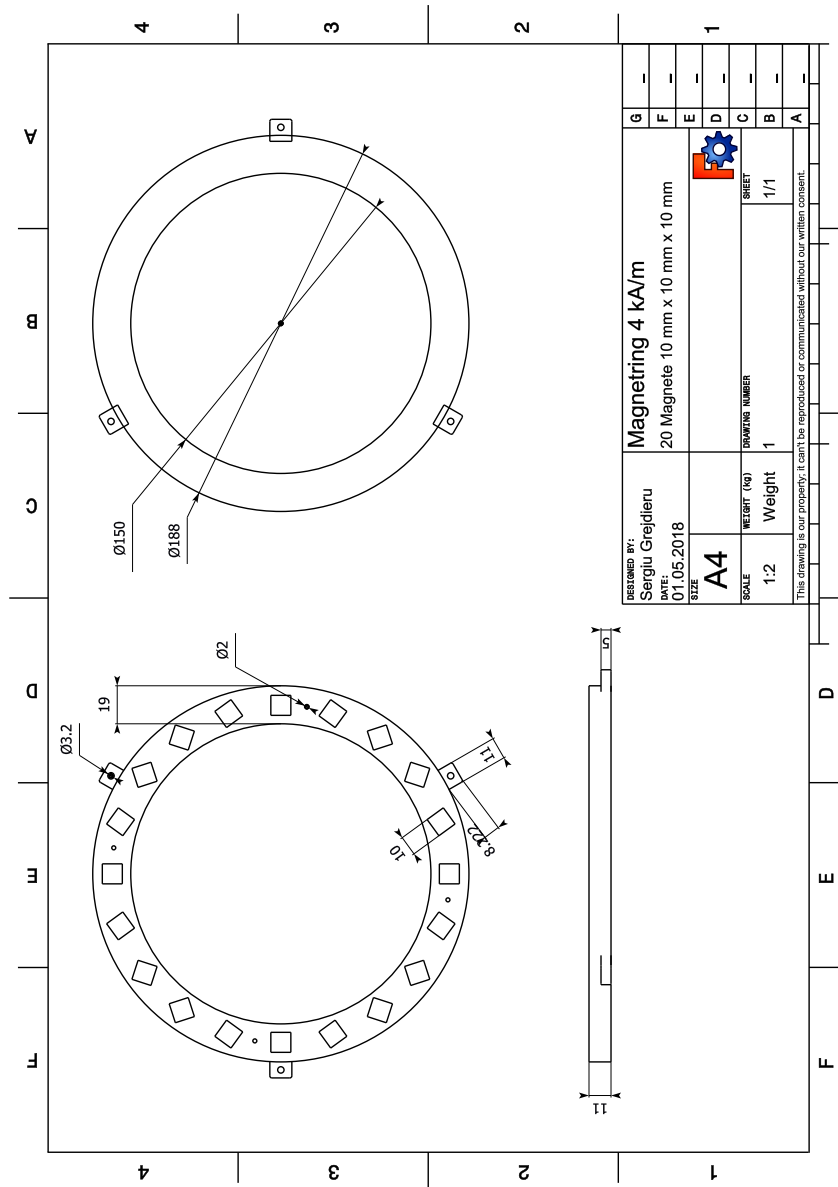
Technische Zeichnung: Magnetring 4 kA/m
